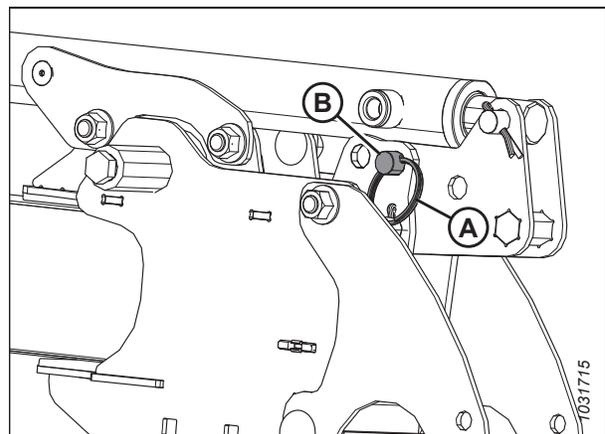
Cilindro del braccio destro – Posizione avanzata
